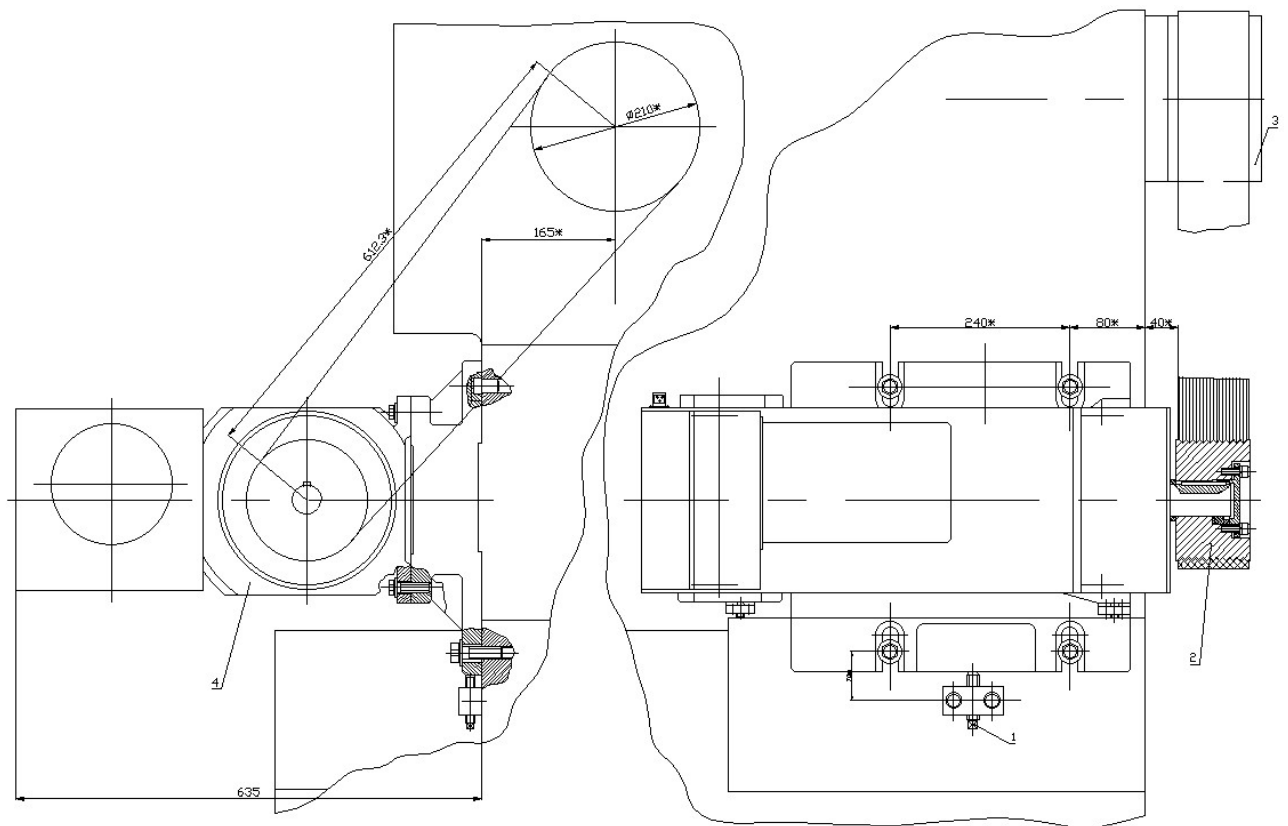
Привод головного руху токарно-револьверного верстата.
